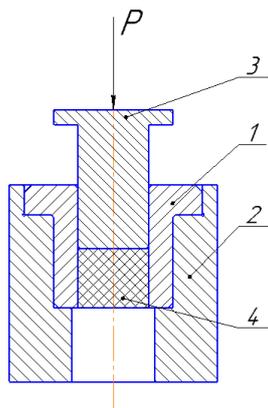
Схема проведения испытаний с использованием приспособления в сборе:
